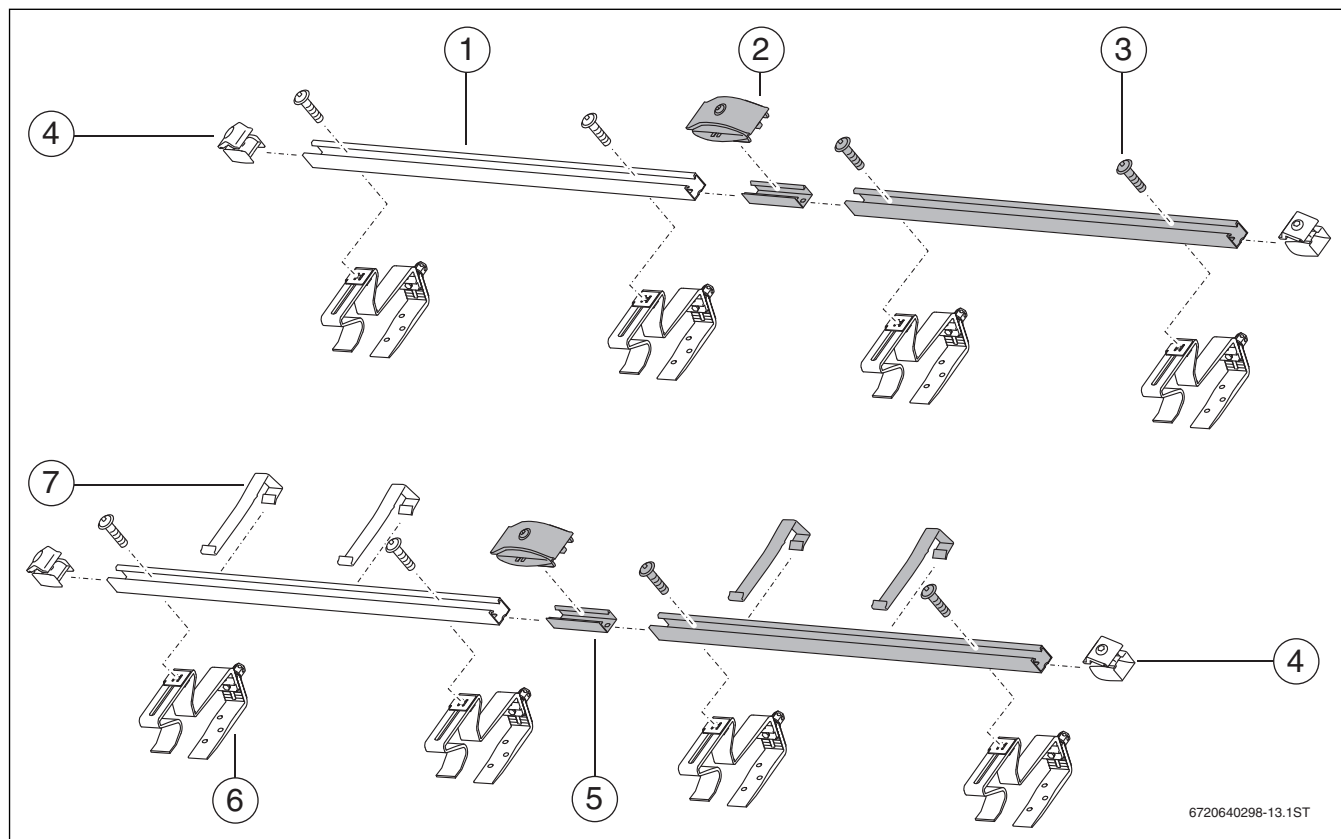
Montage-Set für 2 Kollektoren: 1 Montage-Set Grundauführung, 1 Montage-Set Erweiterung (grau) und 2 Montage-Sets für Dachziegel
